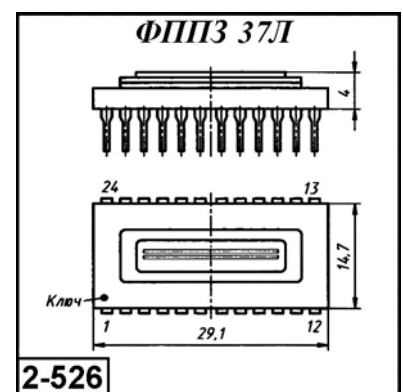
Внешний вид и габаритные размеры ФППЗ 37Л
